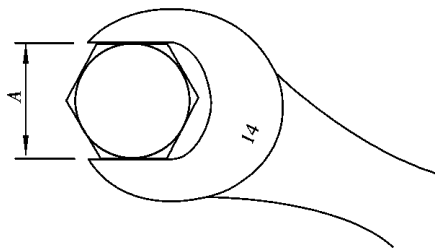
扳手的尺寸,“A”是横跨螺母或螺栓头对边的尺寸
